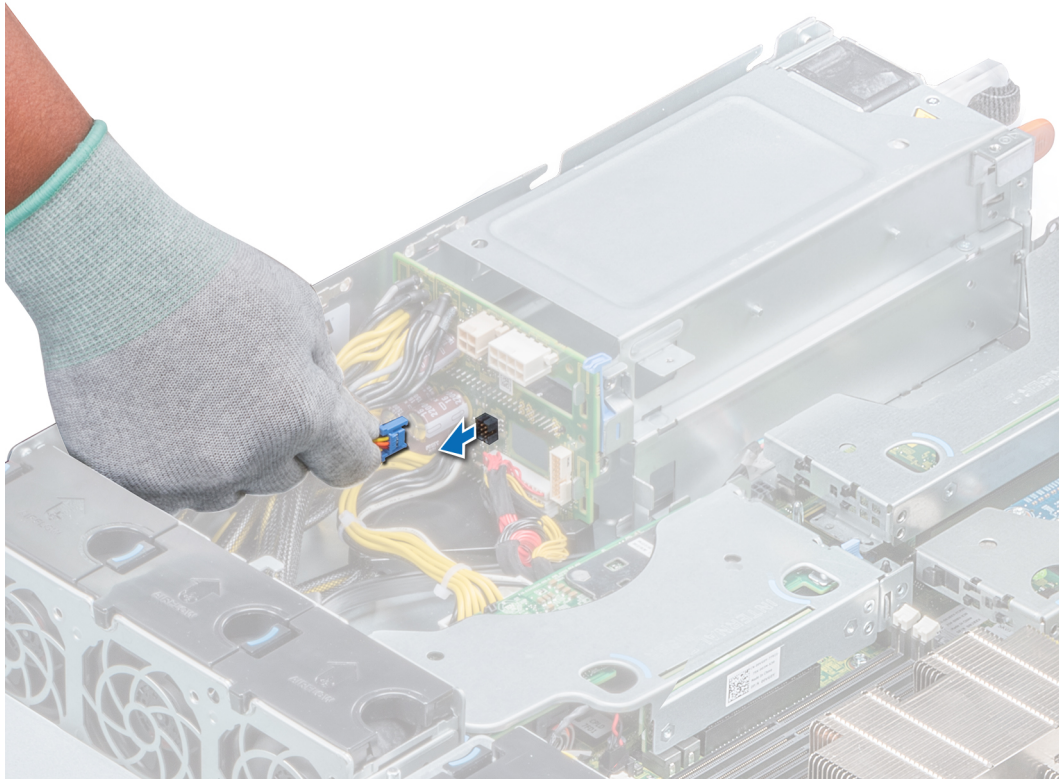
Desconexión del cable del ventilador al conector de la PIB
